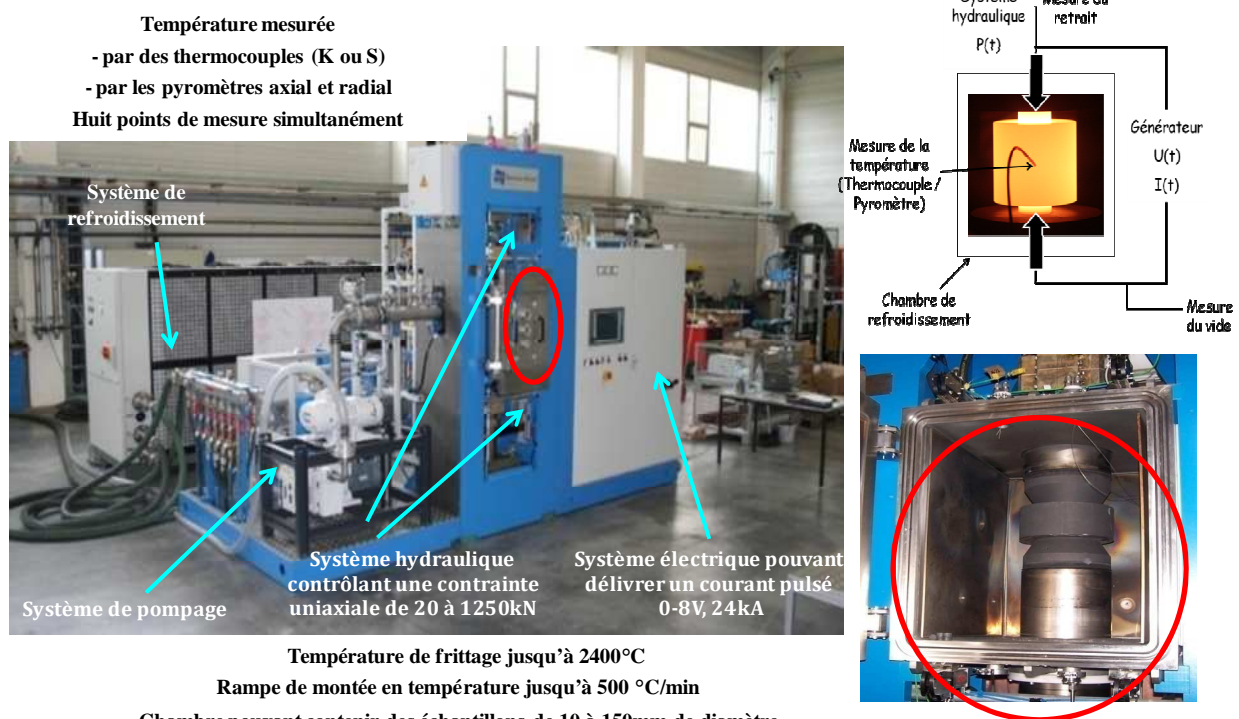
Vue d'ensemble de la machine SPS installée à Dijon, HPD 125 et schéma de principe du frittage SPS.
